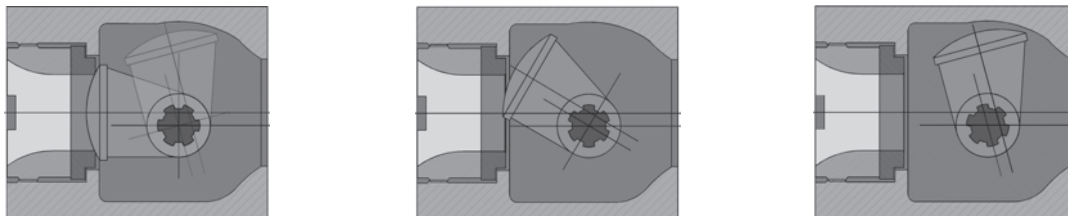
· Vue en coupe : déplacement du clapet pour position à double excentration
